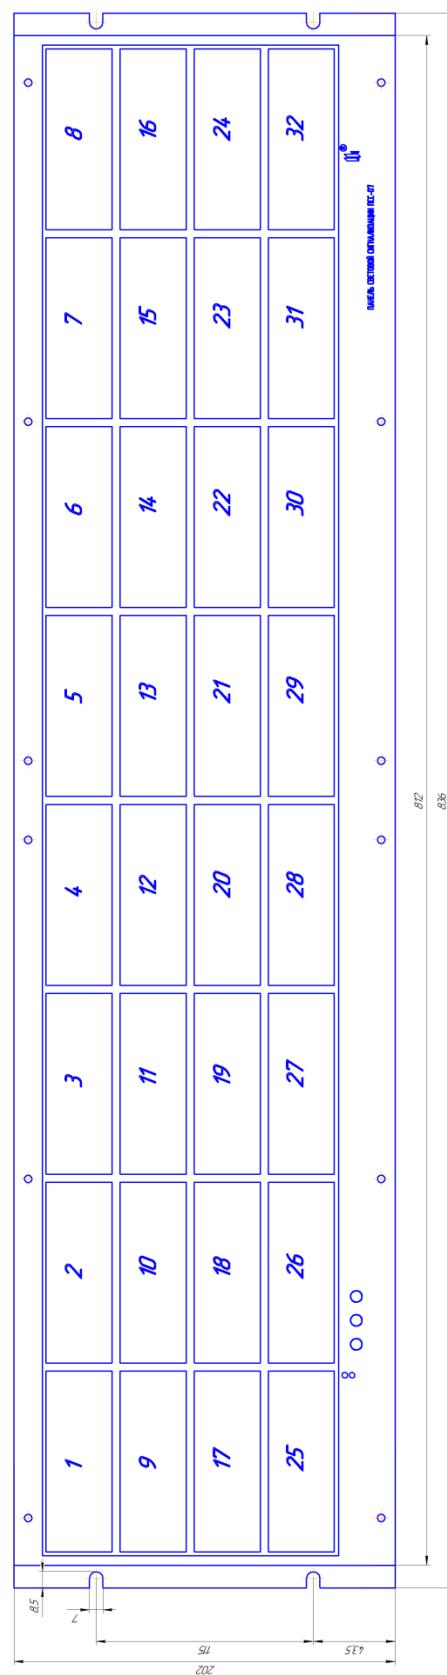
Габаритные размеры ПСС-07-08
